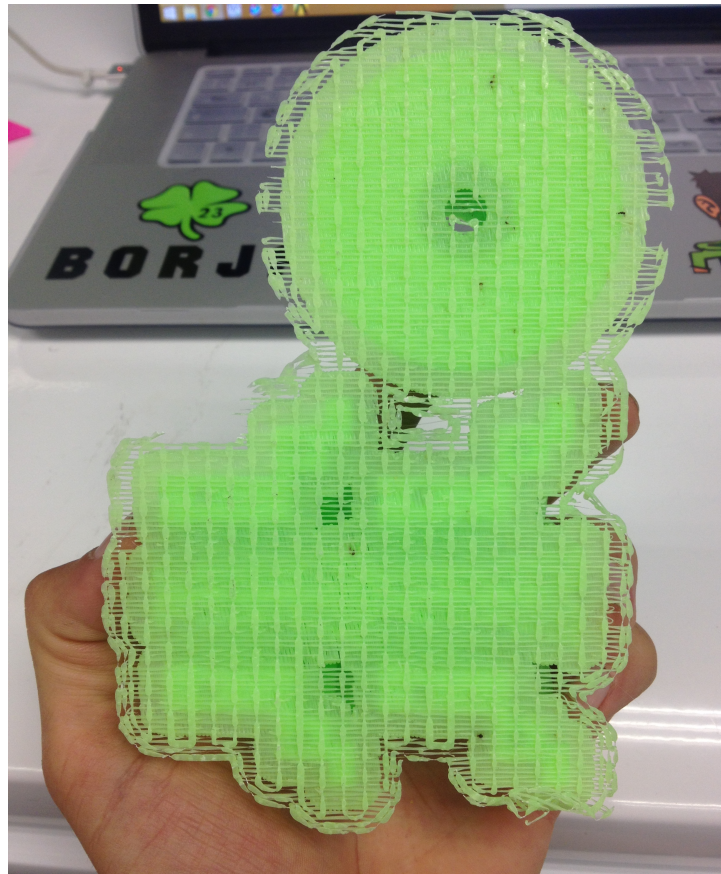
Fabricación del Molde. Vista trasera del molde acabado. (Fuente: Propia)
